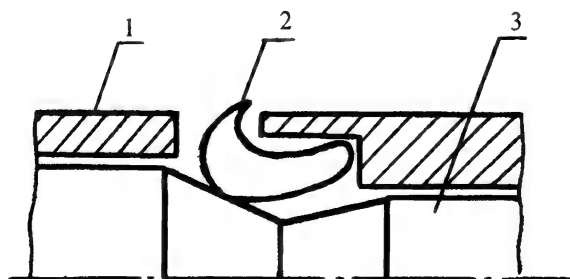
Конструктивная схема крючкового шпалера: 1 - трубка, 2 - крючок (резец), 3 - клин
